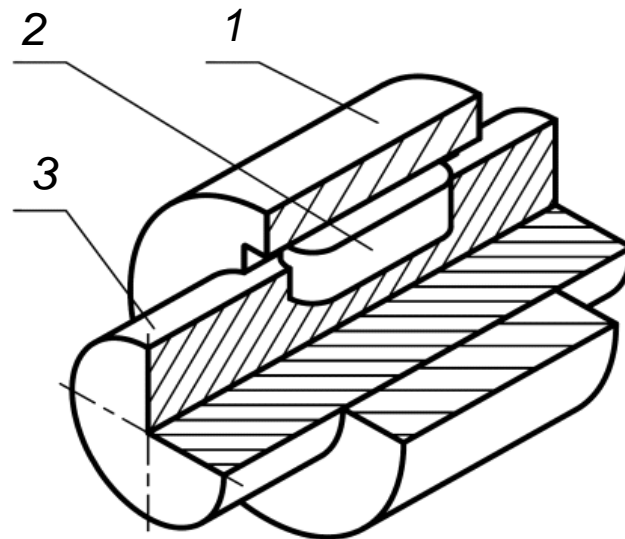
Шпонкове з'єднання: 1 – втулка; 2 – шпонка; 3 – вал
